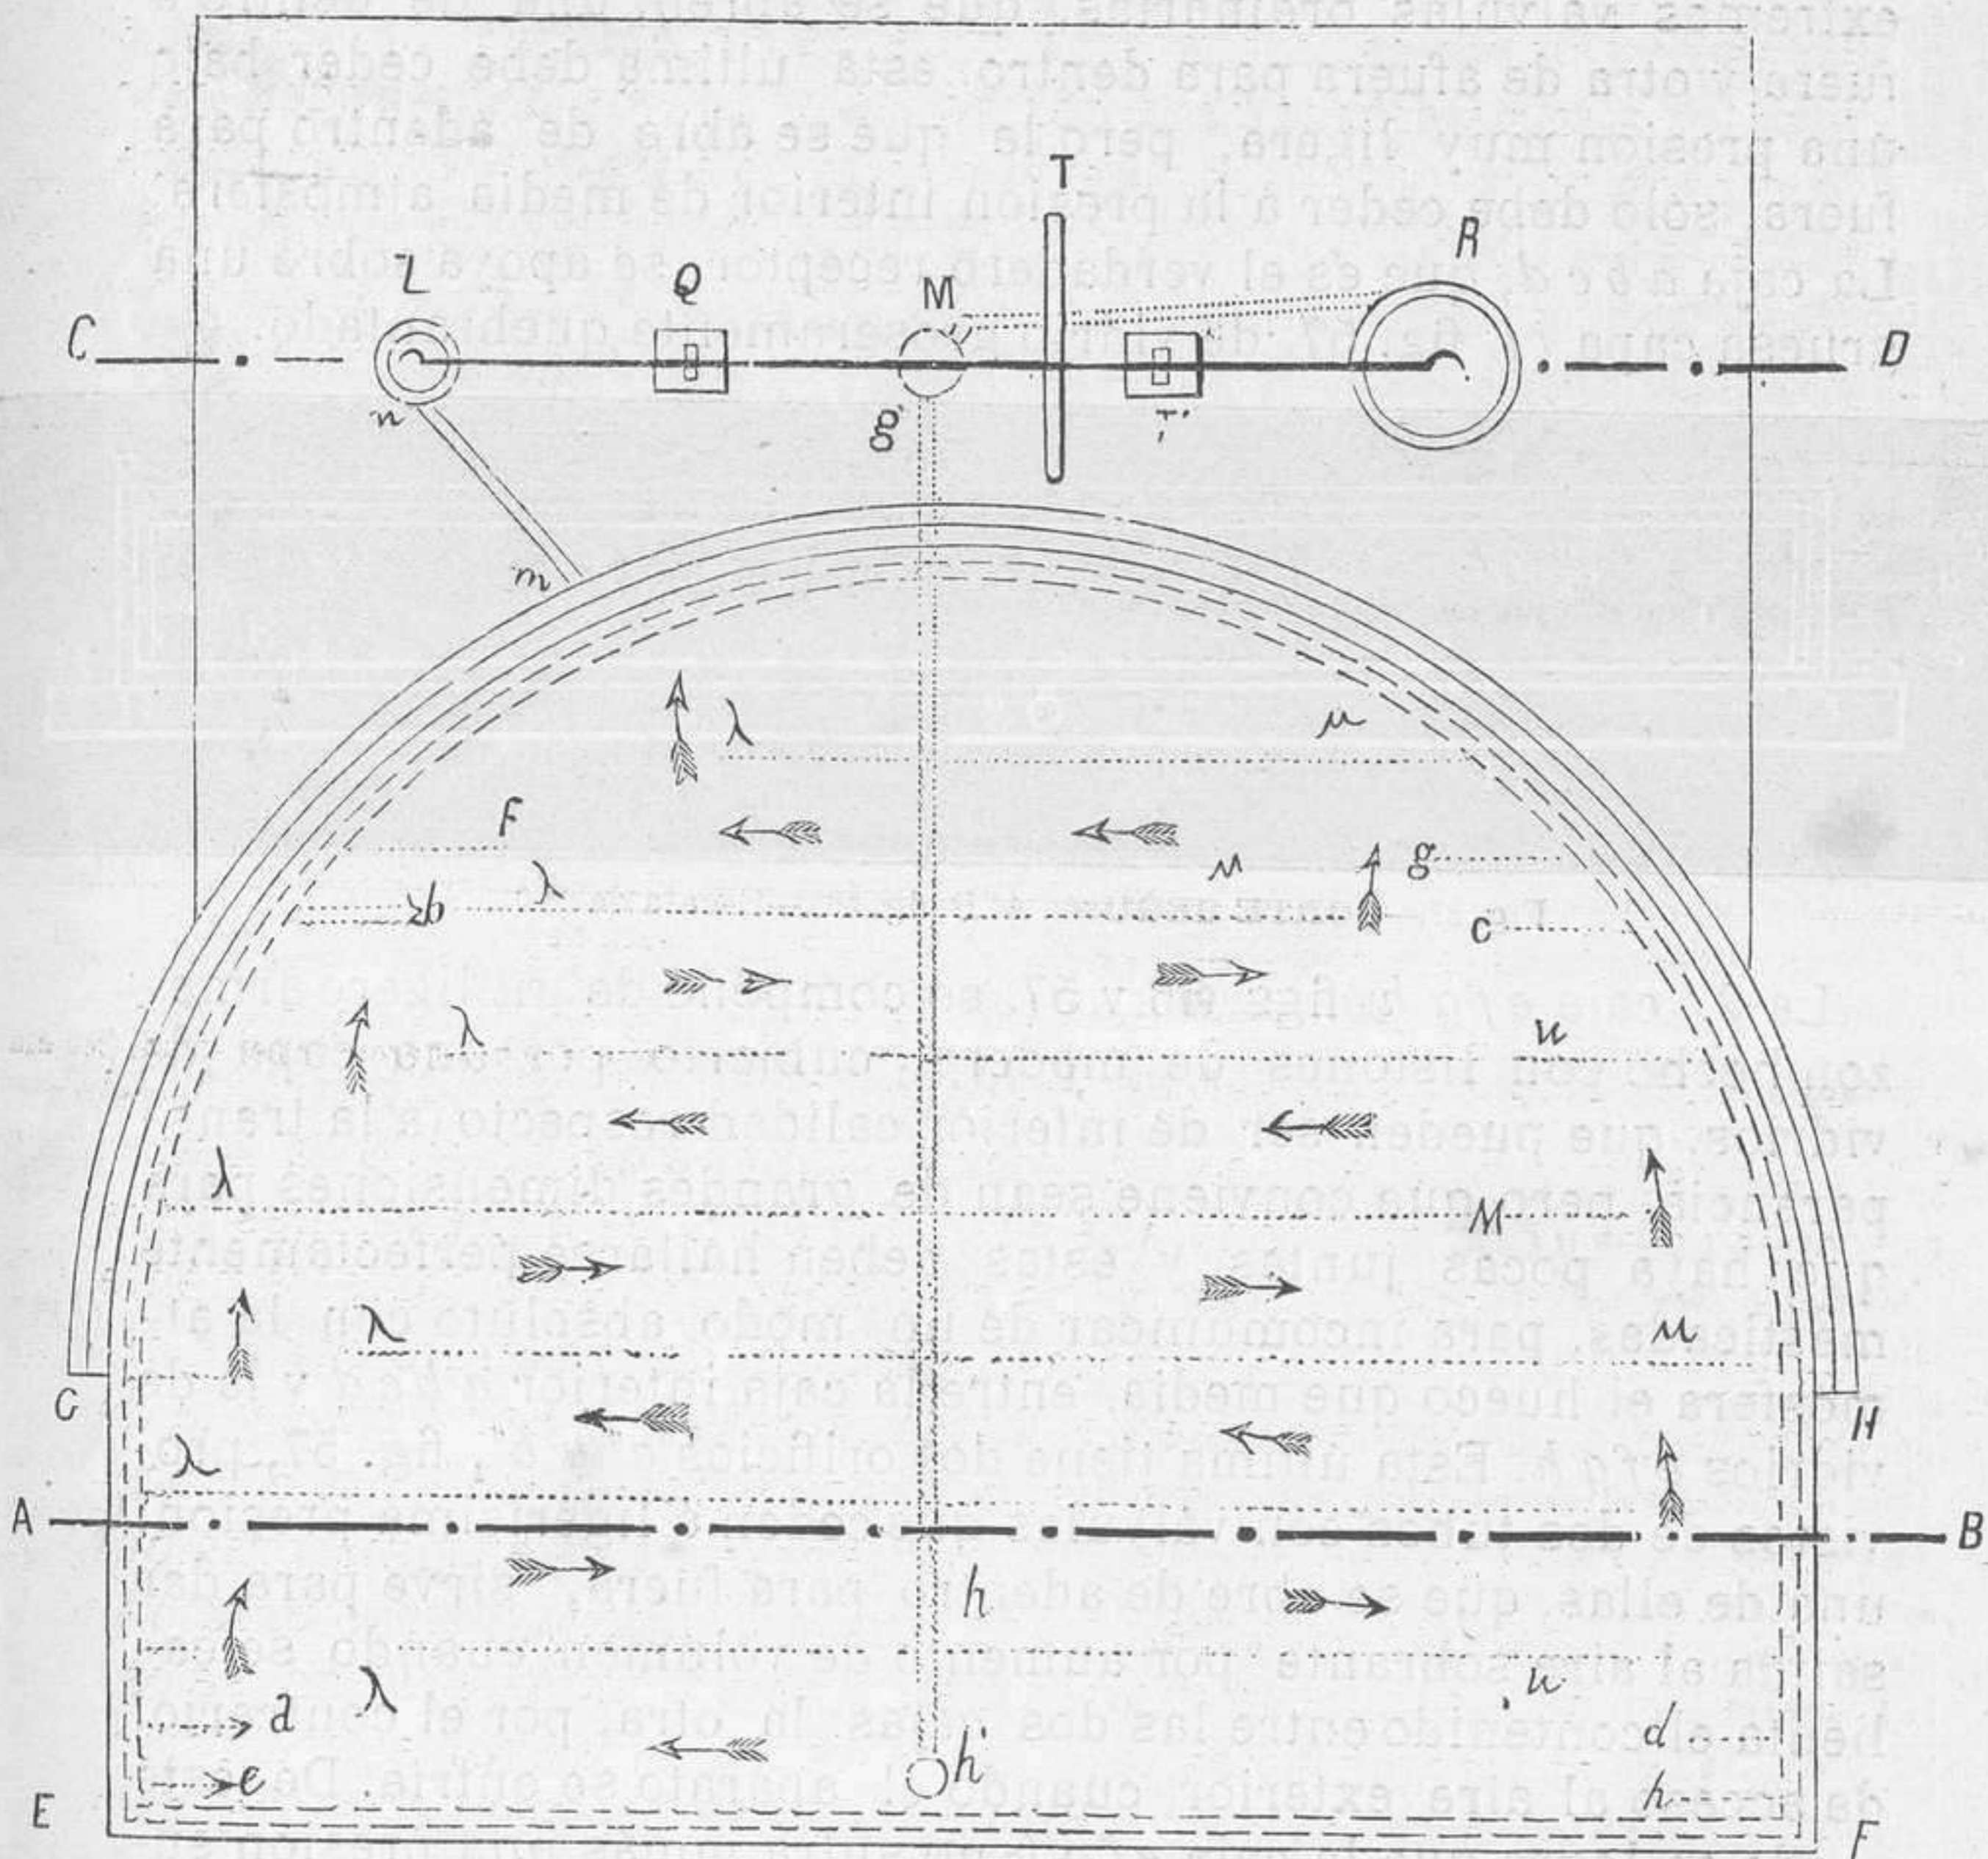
CORTE HORIZONTAL DEL MOTOR.—Escala de 0^m,01 por metro.
